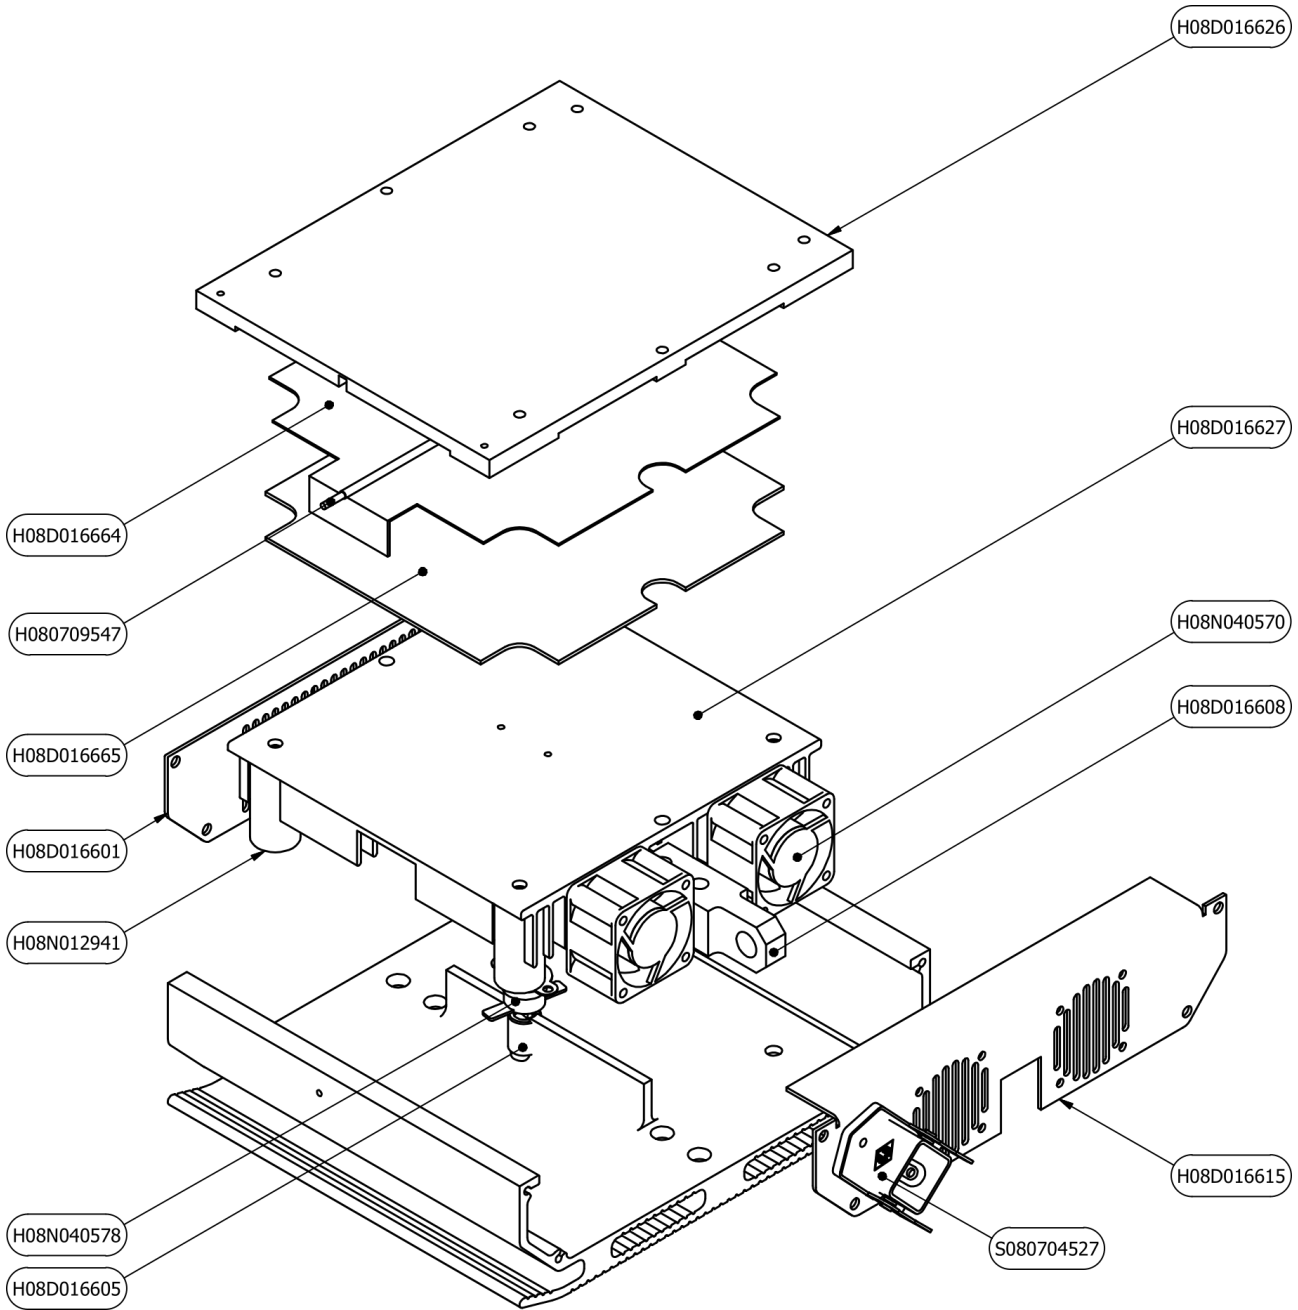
H08D016628 Assemblage de la plaque chauffante inférieure PML-100
